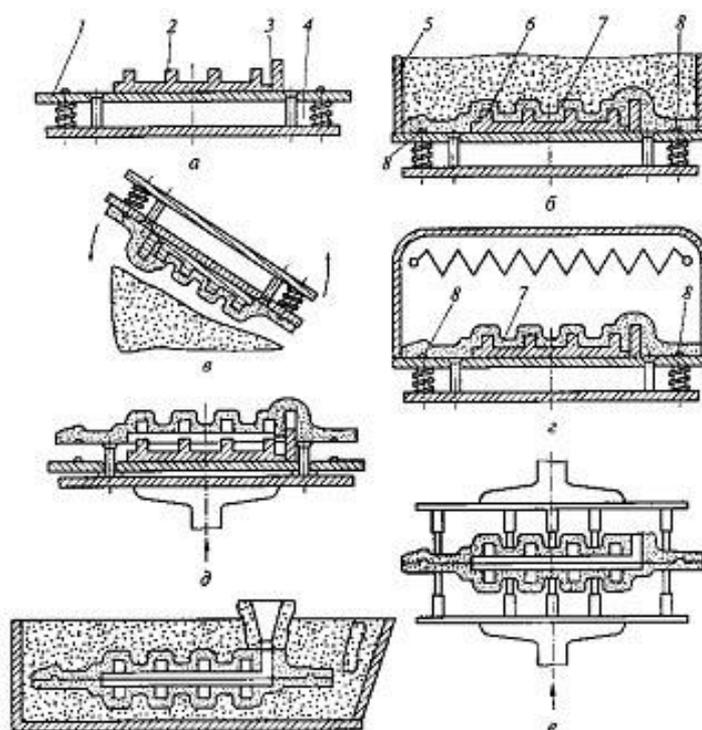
Схема технологического процесса изготовления оболочковых форм:
